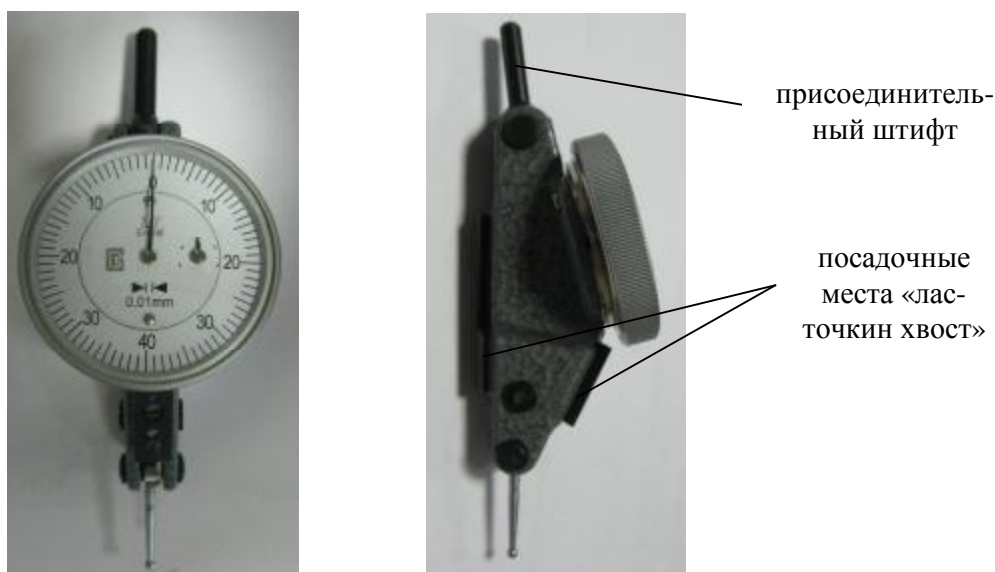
Общий вид индикаторов рычажно-зубчатых ИРБ тип II
